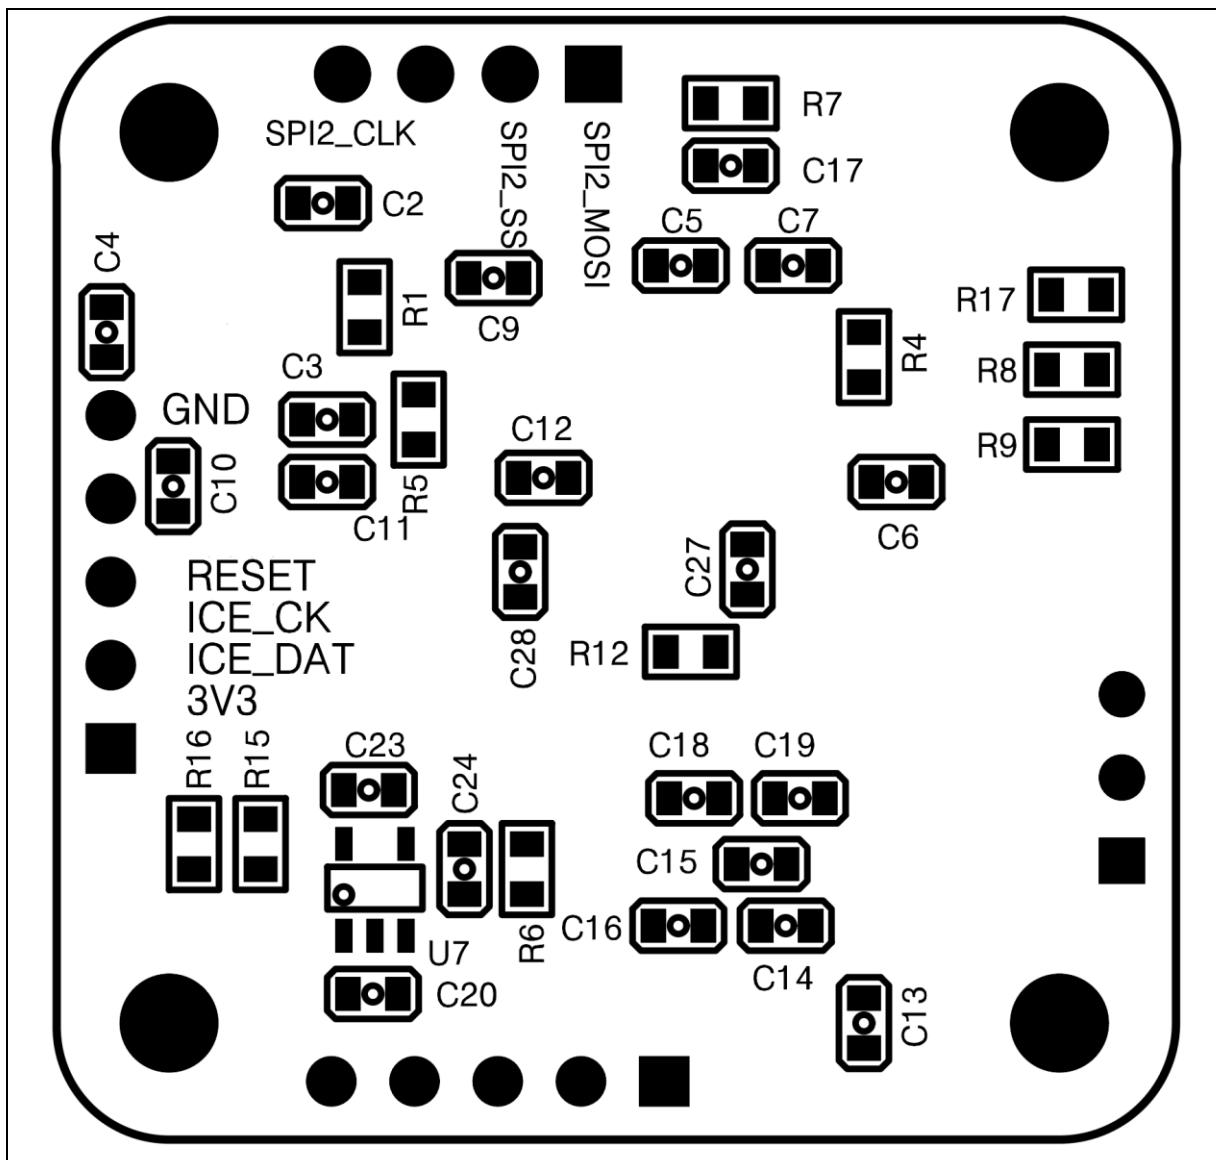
AHRS 模組主控端反面 PCB 佈局
